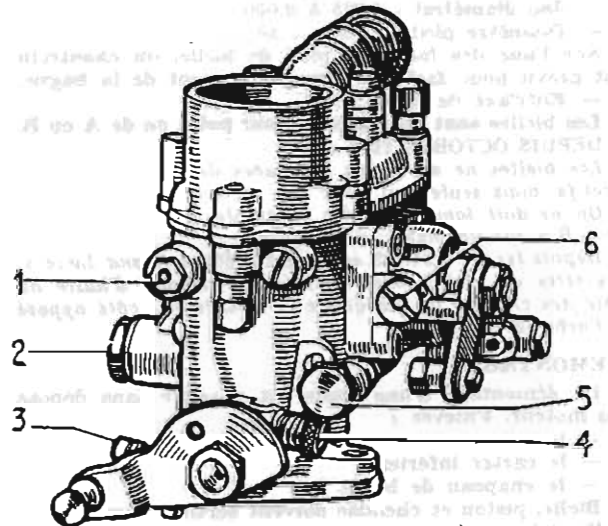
VUE DU CARBURATEUR 22 BIC
